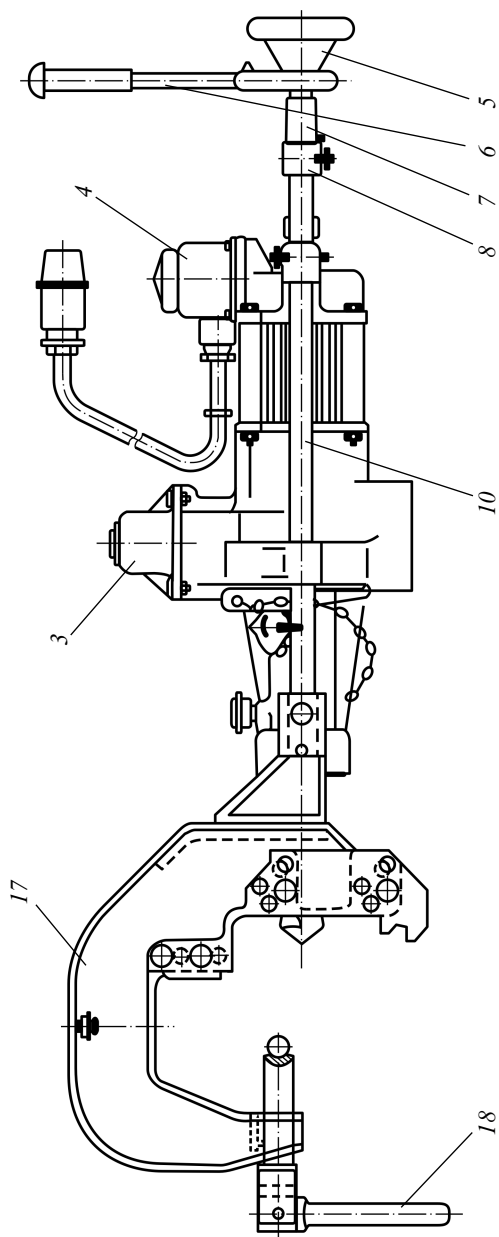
Рельсосоверлильный станок 1024В с верхним захватом:
